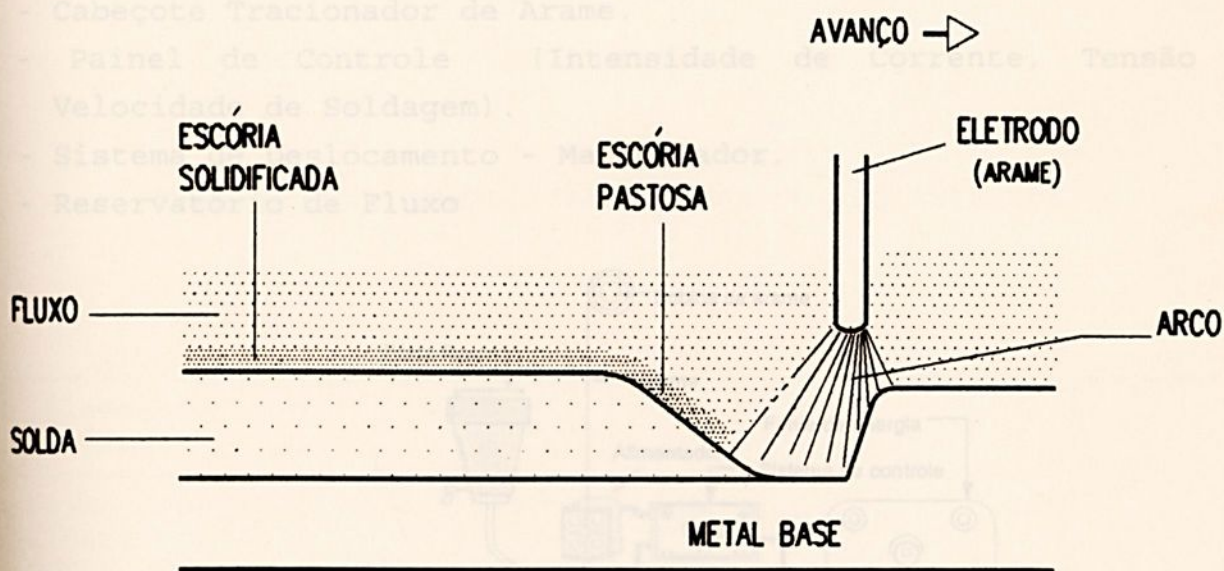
Soldagem ao Arco Submerso - esquemático.
